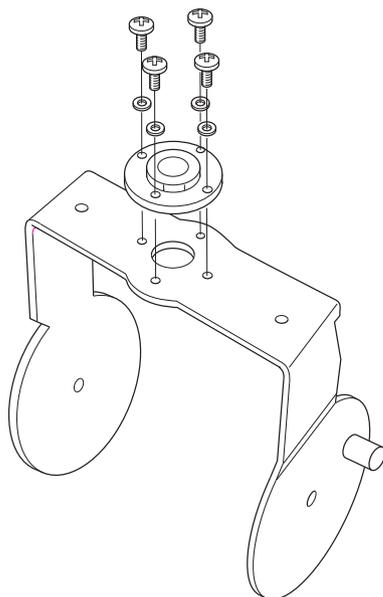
Installazione della piastra alla staffa di sospensione in caso di montaggio su una base da terra.
